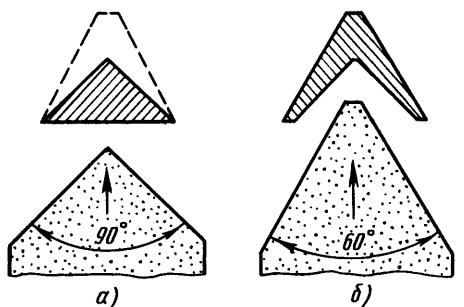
Схема нарезания резьбы блоком из двух резцов — чернового (а) и чистового (б)
